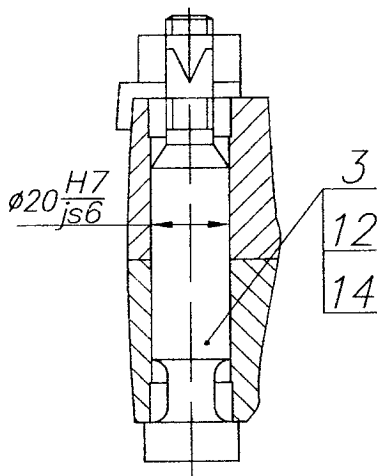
Фрагмент креслення елементів конструкції для центрування верхньої і нижньої половин діафрагми:
